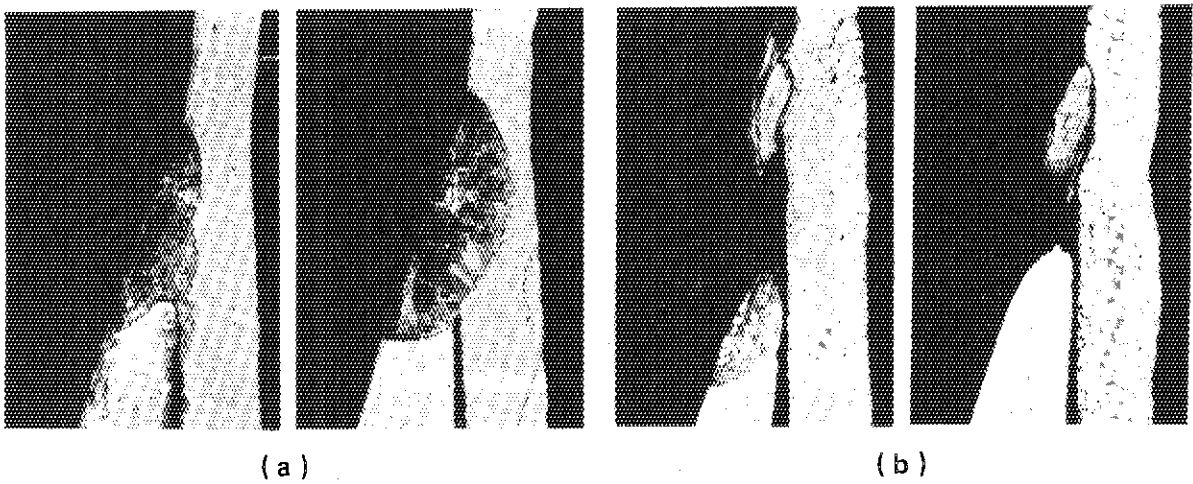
引張試験後のシール溶接部断面 ; (a) ステン
